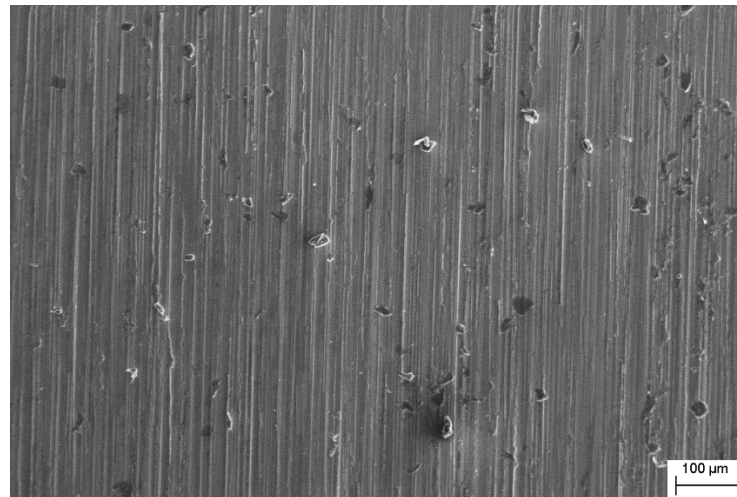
Peça retificada com 1,00 mm/min de avanço, para o rebolo CBN HF.
